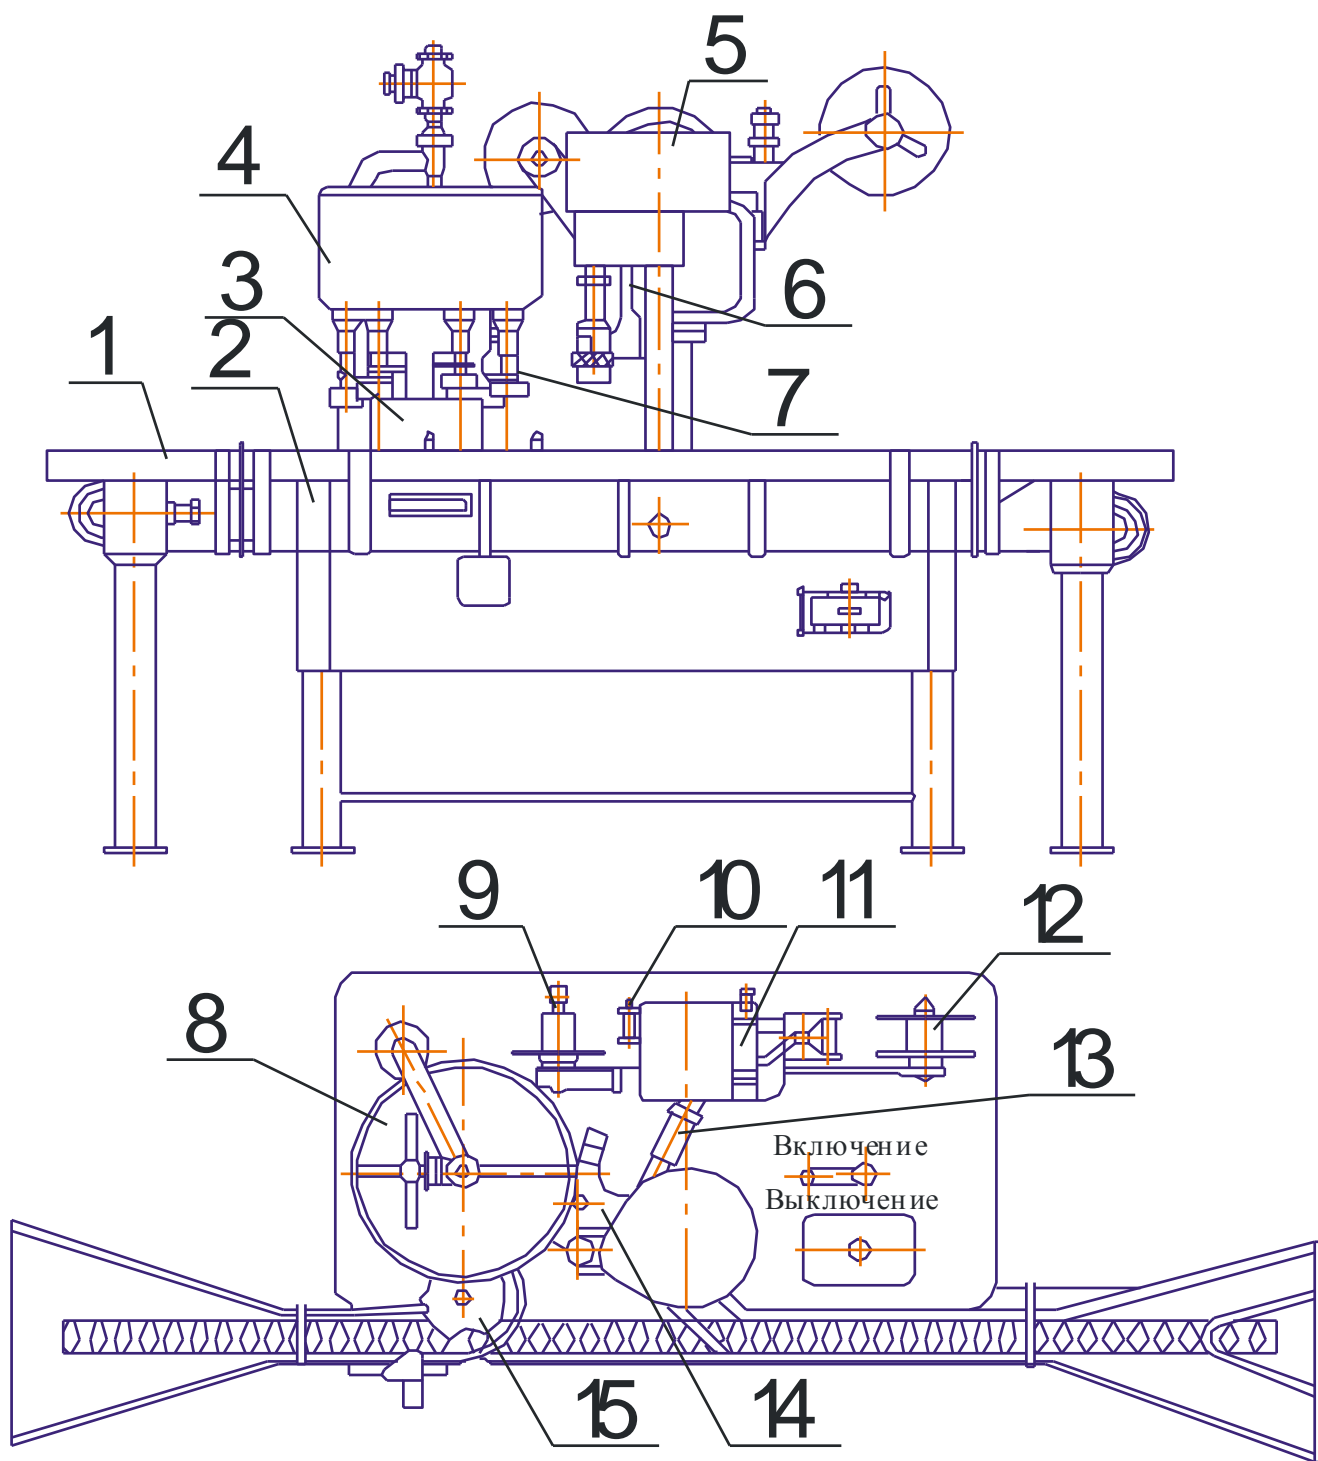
Общий вид фасовочно-укупорочной машины.
